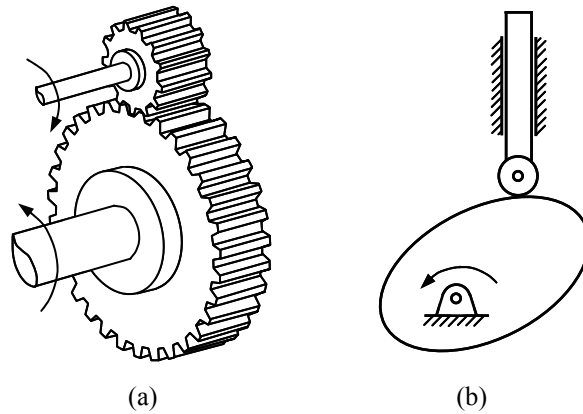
Transmissão de movimento por contacto directo: (a) Sistema de engrenagens; (b) Mecanismo came-seguidor.
